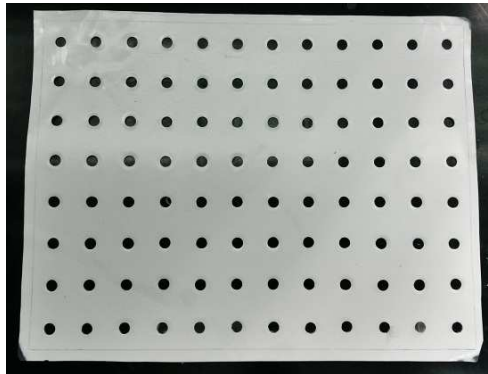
Заготовка відбивача світла з отворами під лунки
